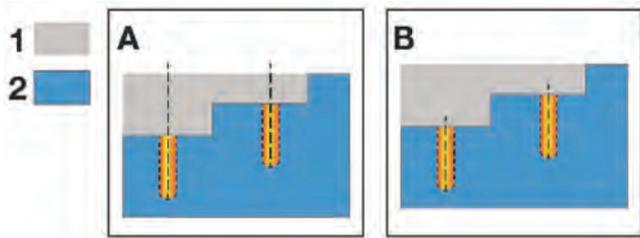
Пример с учетом цикла сверления. [1] Модель заготовки, [2] Модель детали. [A] Параметр «Использовать Предыдущую Заготовку» включен. Цикл сверления начинается выше необработанной заготовки. [B] «Использовать Предыдущую Заготовку» отключен. Цикл сверления начинается внутри необработанной заготовки.
